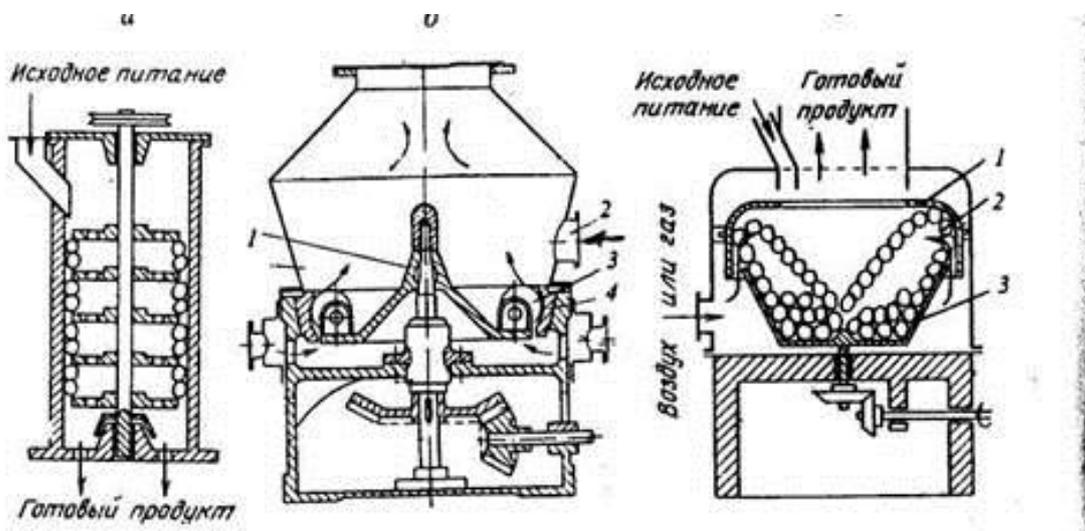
Схемы центробежных мельниц: барабанной (а), шарокольцевой (б) и центробежно-шаровой (в)
